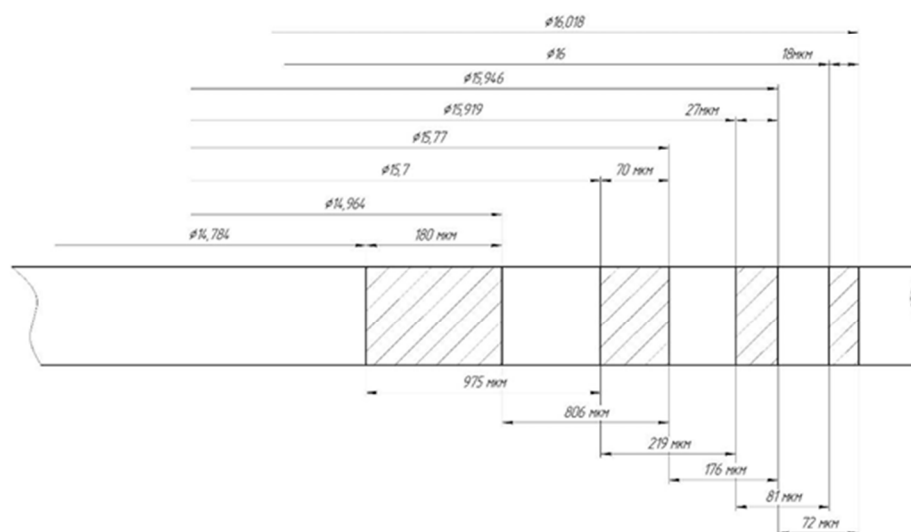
Схема розташування припусків і допусків на обробку отвору $\varnothing 16H7^{+0,018}$
